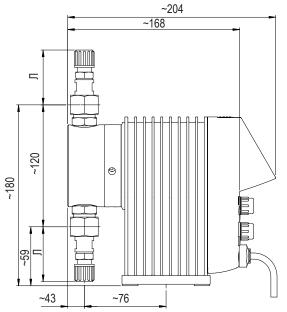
Габаритный чертеж MAGDOS LK/LP Размерный чертёж с дозирующей головкой из ПВХ, ПП или ПВДФ
